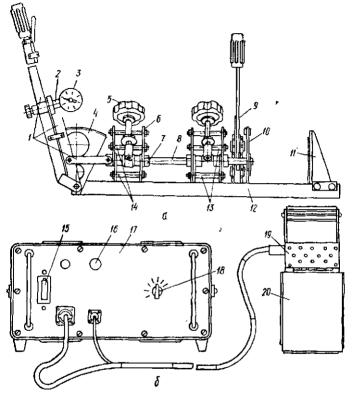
Установка УСТТ-110 для сварки пластмассовых труб: а — центратор с торцовочным устройством; б — блок управления с нагревательным инструментом.
